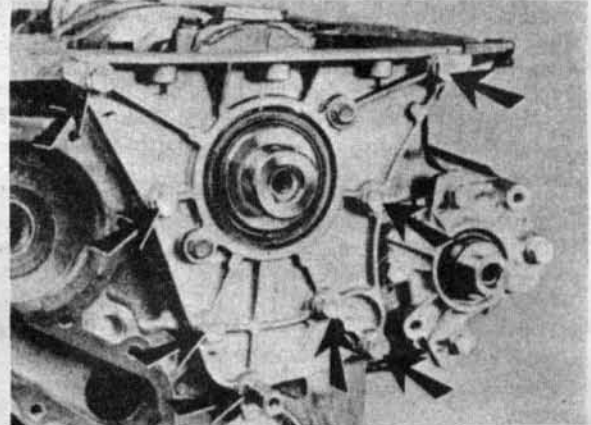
Болты крепления крышки блока со стороны привода механизма газораспределения
